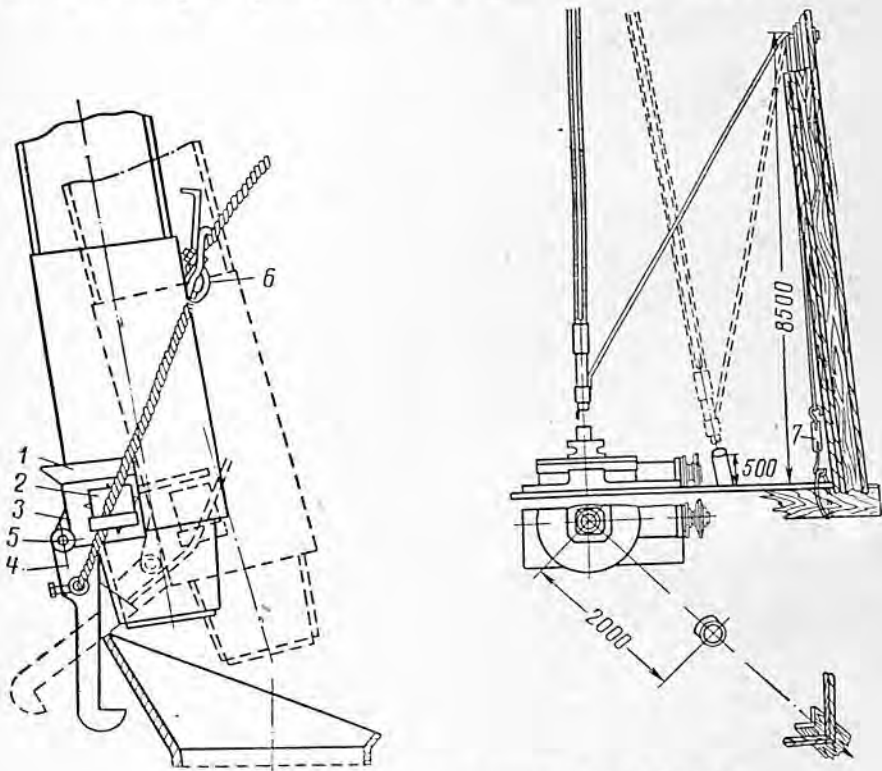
Автозатаскиватель ведущей трубы в шурф.
